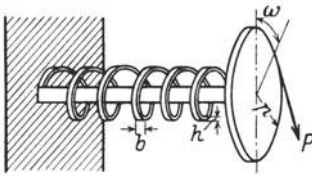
Schraubenfeder mit rechteckigem Querschnitt.
